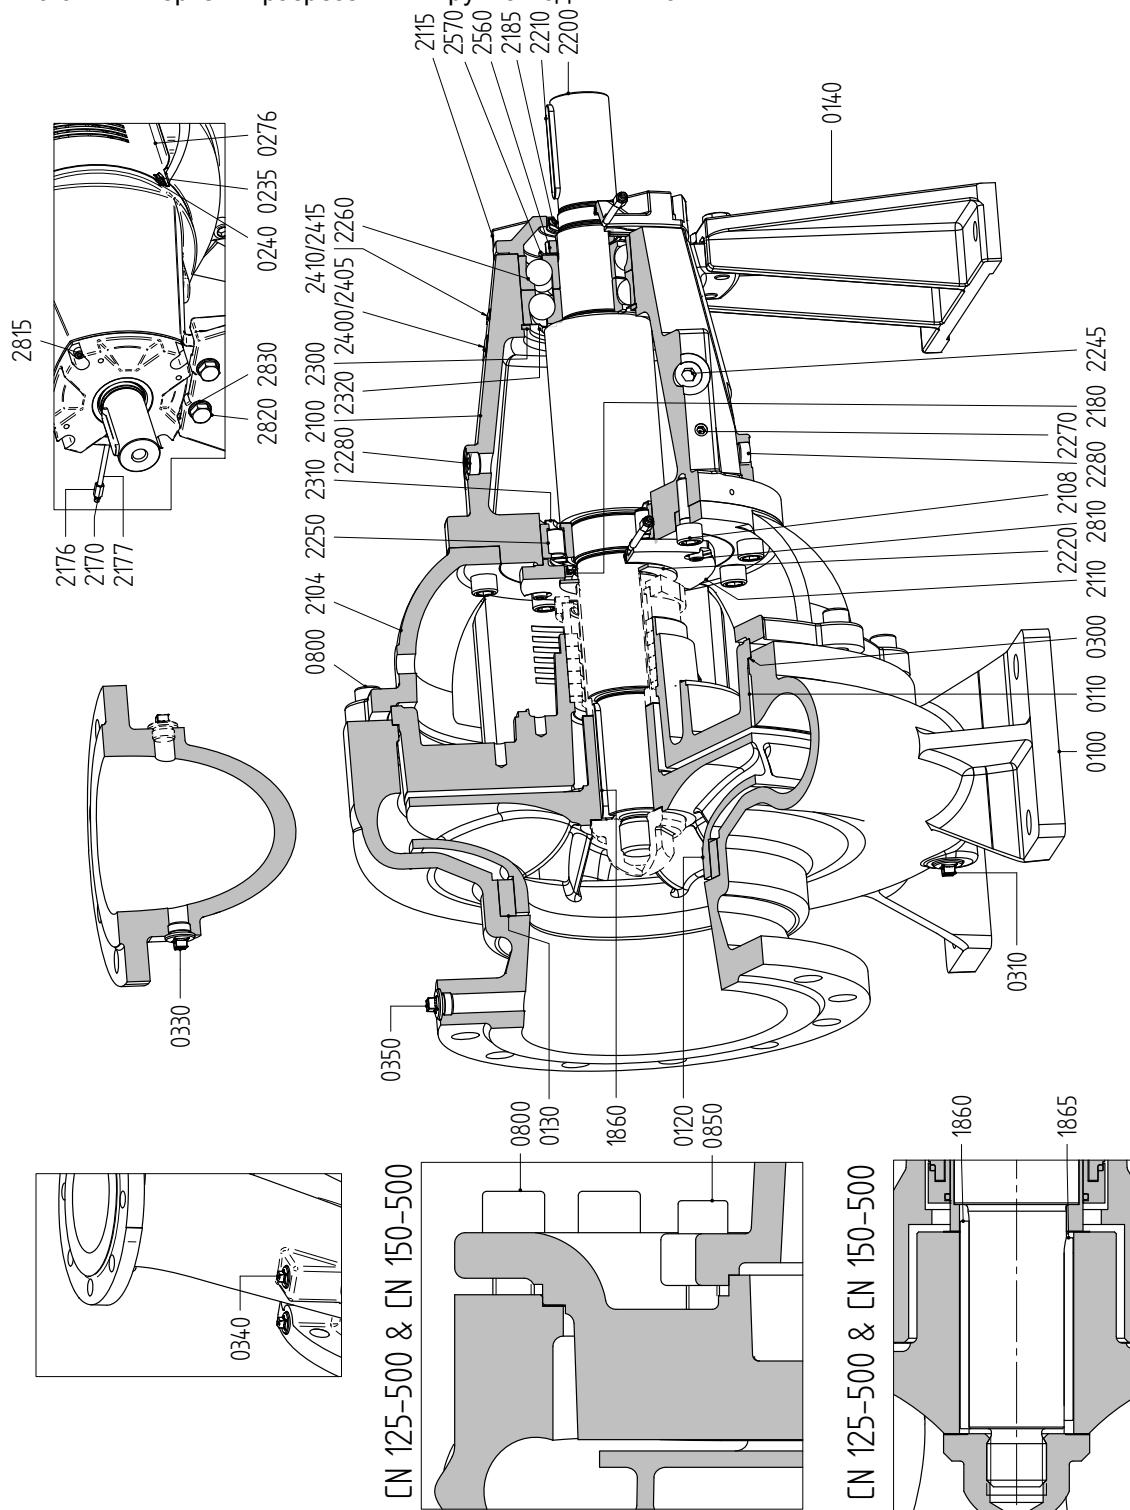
Чертеж в разрезе L2 — группа подшипников 4
